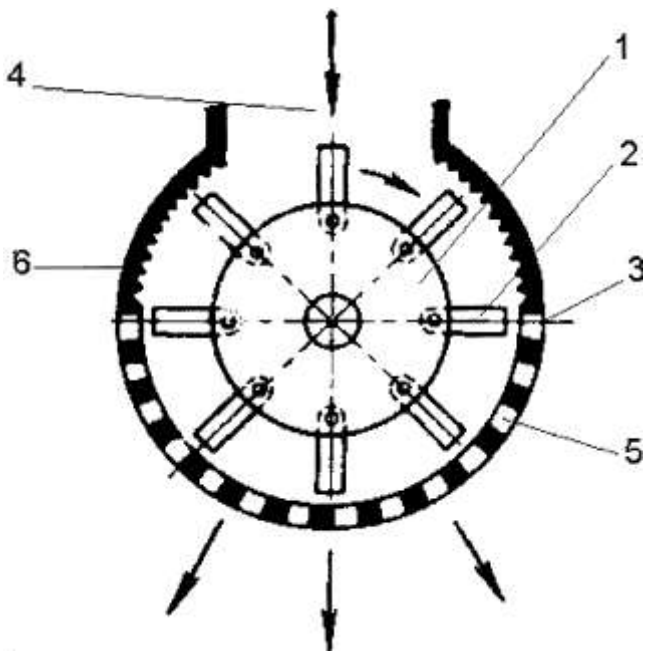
Схема робочого процесу молоткової дробарки: 1 - ротор; 2 - молоток; 3 - корпус; 4 - завантажувальна горловина; 5 - решето; 6 - дека.
